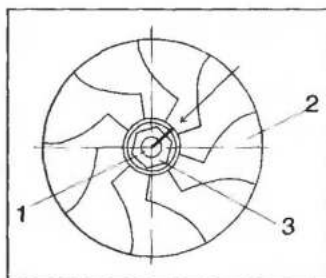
Схема нанесения меток на детали ротора перед отворачиванием гайки - метки на валу, гайке и колесе компрессора должны располагаться на одной линии:
